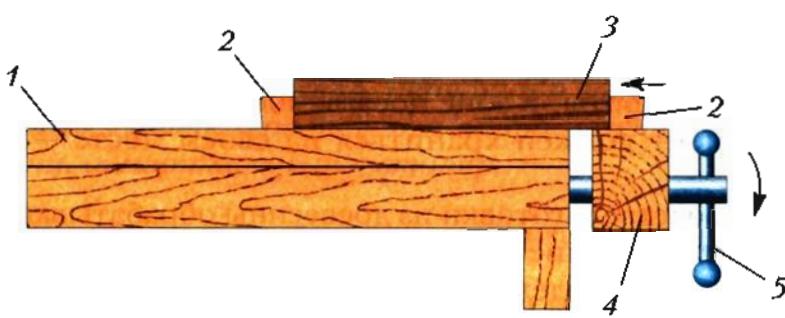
Крепление заготовки на верстаке клиньями с поджатием задним зажимом: 1 — крышка верстака; 2 — клинья; 3 — заготовка; 4 — задний зажим; 5 — рукоятка зажима
